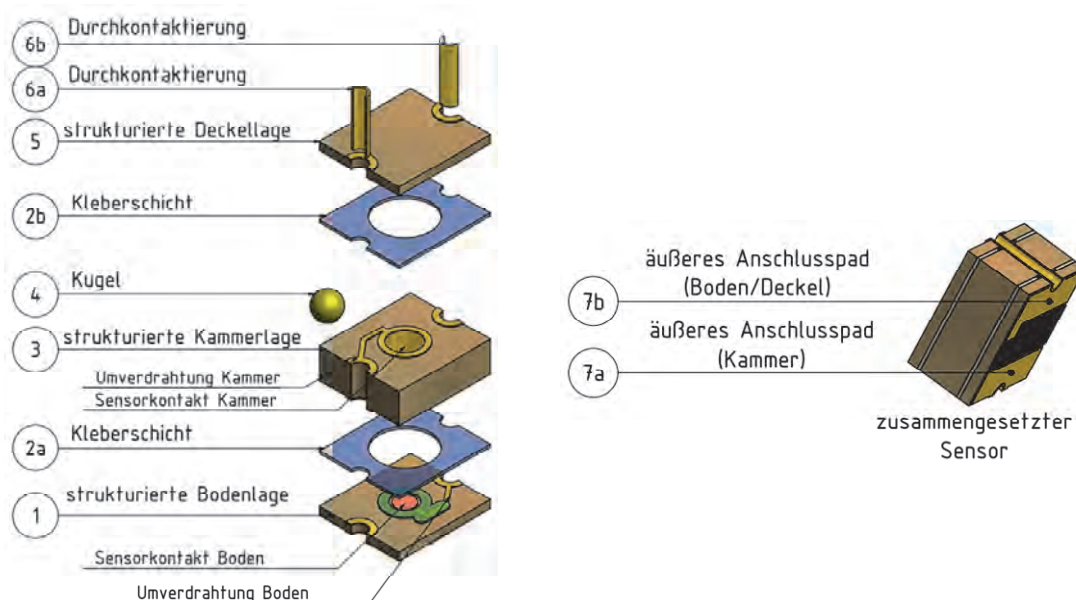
Explosionszeichnung eines Mikro vibrationsschalters in Plattenbauweise. Im linken Teil des Bildes sind die einzelnen Teile des Sensors in einer Explosionszeichnung dargestellt, rechts ist der zusammengesetzte Sensor zu sehen.
